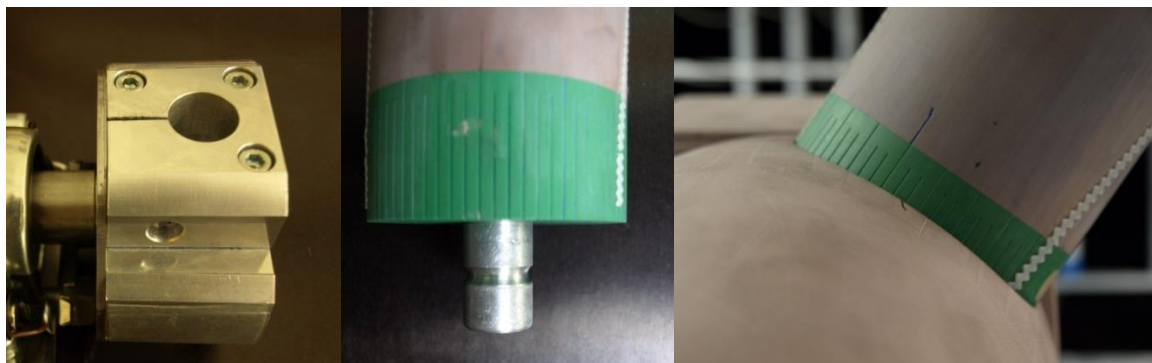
Rotorblattaufhängung (links Rotornabe; Mitte Rotorblatt; rechts Montierter Zustand mit Spinner)
